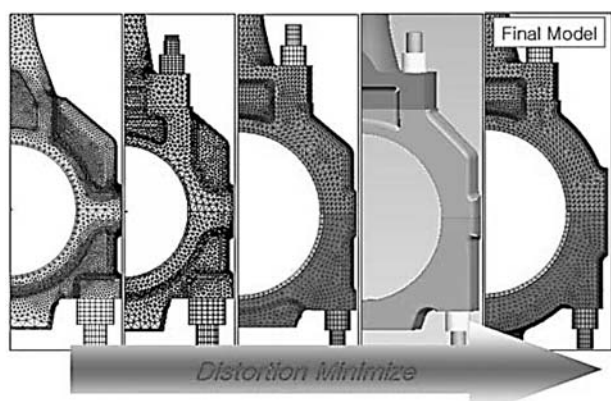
Варианты конструкции шатунного подшипника коленвала (стрелка показывает направление увеличения жесткости по мере совершенствования конструкции, справа — окончательный вариант)
